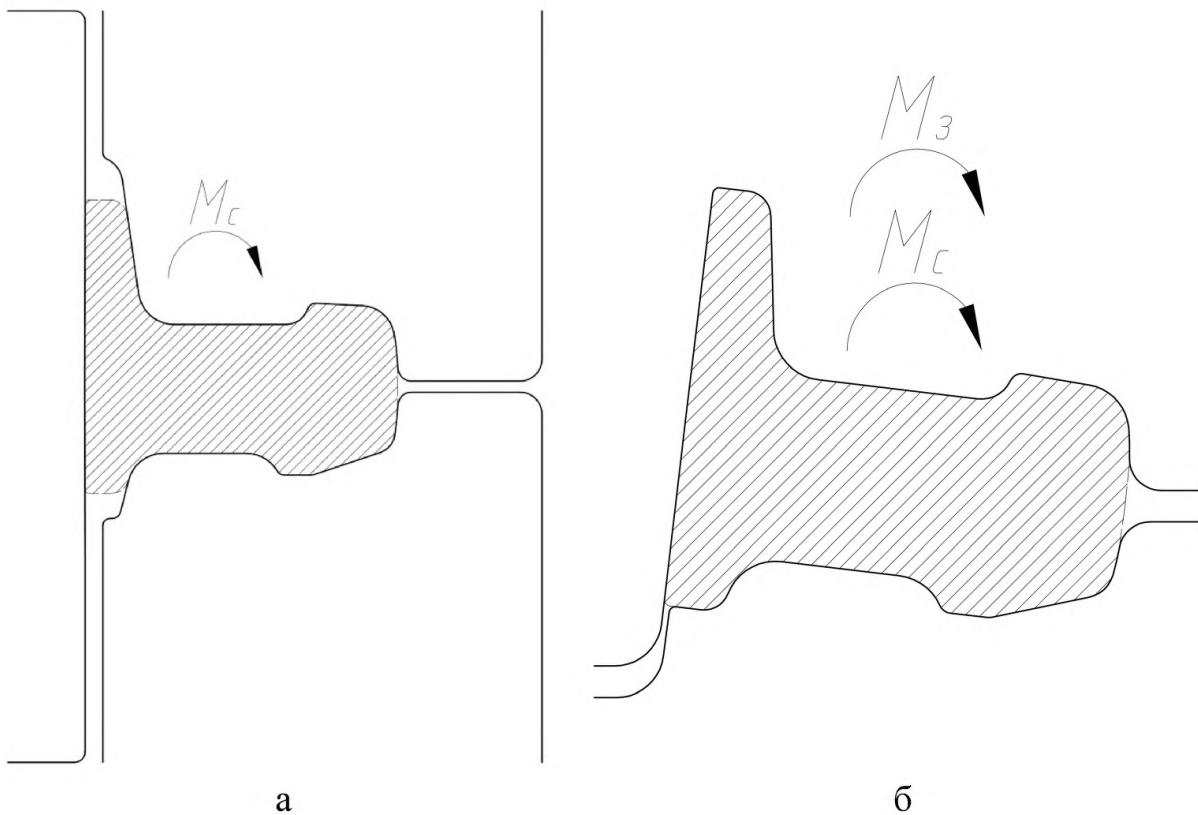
Общий вид универсального трехвалкового (а) и чистового двухвалкового (б) калибров для прокатки рельсов остряковых
